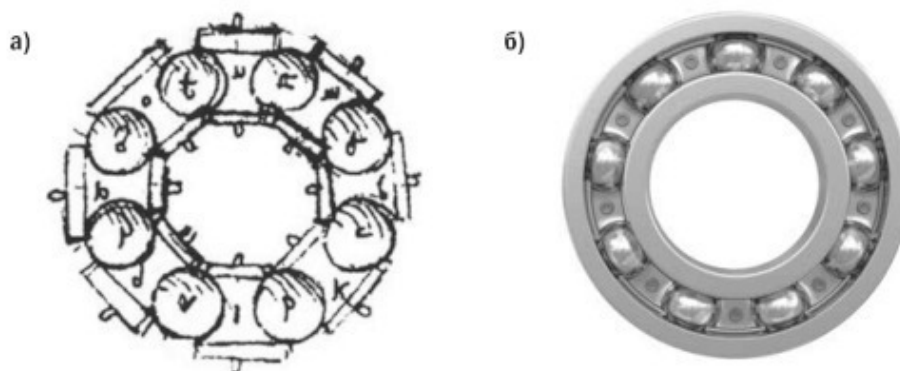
Шариковый подшипник: а – предложенный Леонардо да Винчи; б – современный
